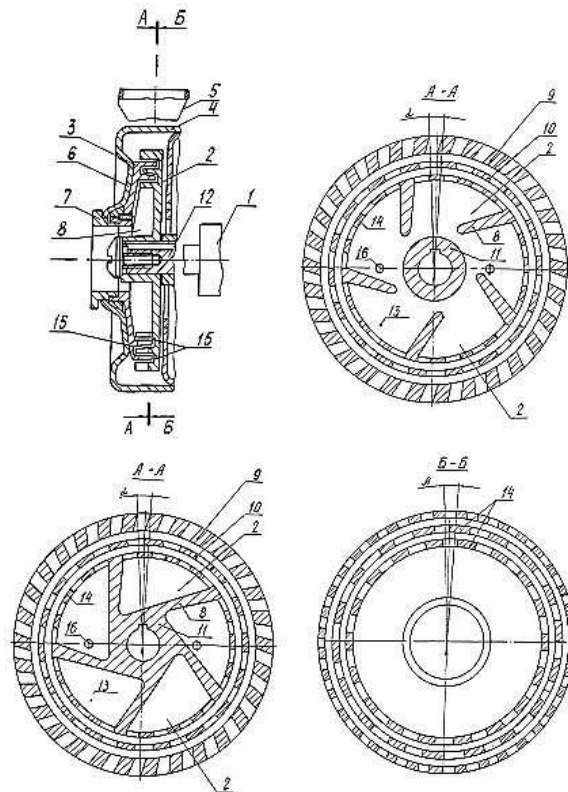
Загальний вигляд і в розрізі по перерізах РПА: 1 – привід; 2 – ротор; 3 – статор; 4 – корпус; 5 – випускний патрубок; 6 – кришка; 7 – впускний патрубок; 8 – вхідні лопатки насоса; 9 – вихідні лопатки насоса; 10, 14 – зубчастий елемент; 11 – маточина; 12 – вал; 13 – камера; 15 – кільцеві канавки; 16 – розвантажувальні отвори
